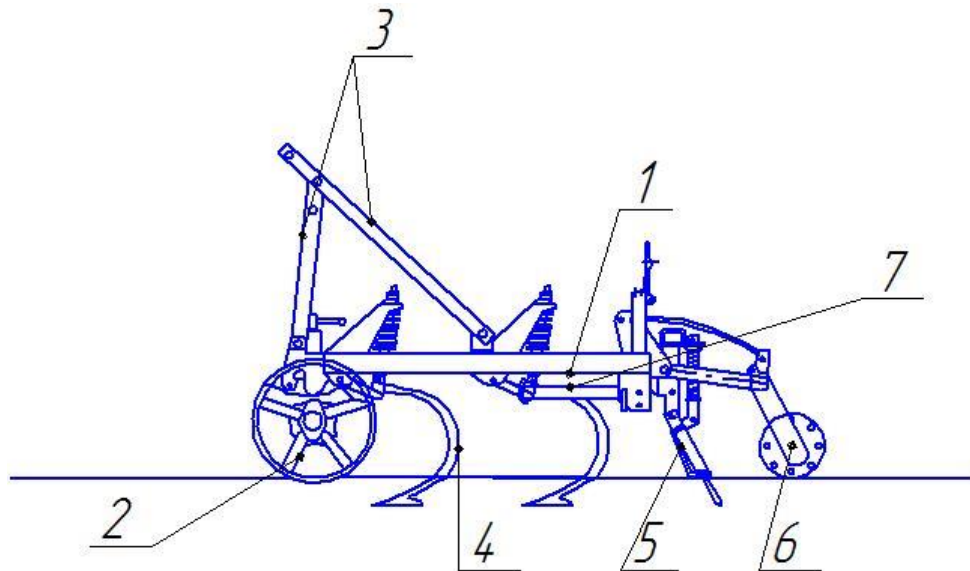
Культиватор комбінований КНК - 4Т: 1 – рама; 2 – опорне колесо; 3 – навісний пристрій; 4 – механізм навішування; 5 – вирівнювач ґрунту; 6 – прикочувальний пристрій; 7 – стійка.
